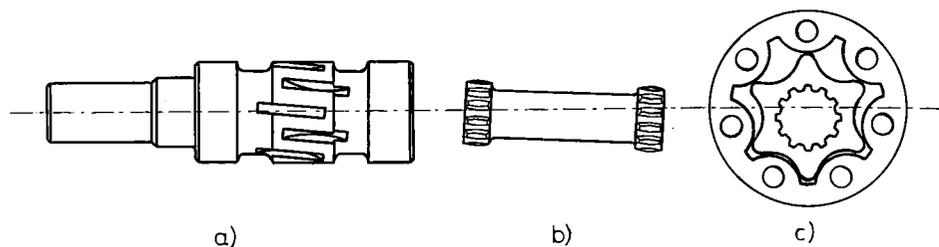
Elementos principales de un motor de engranaje interno: a) eje de salida y carrete distribuidor; b) eje interno; c) conjunto corona-engranaje.
